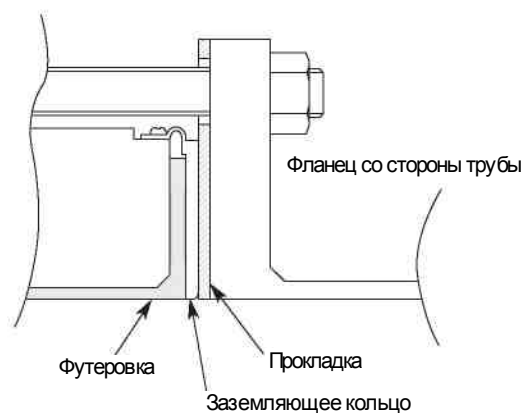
Установка с заземляющим кольцом из нерж. стали и металлической трубой
